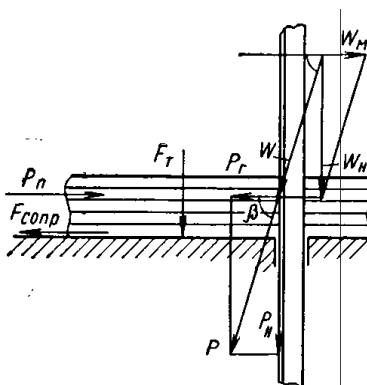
Схема вирізання деталей стрічковим ножем
